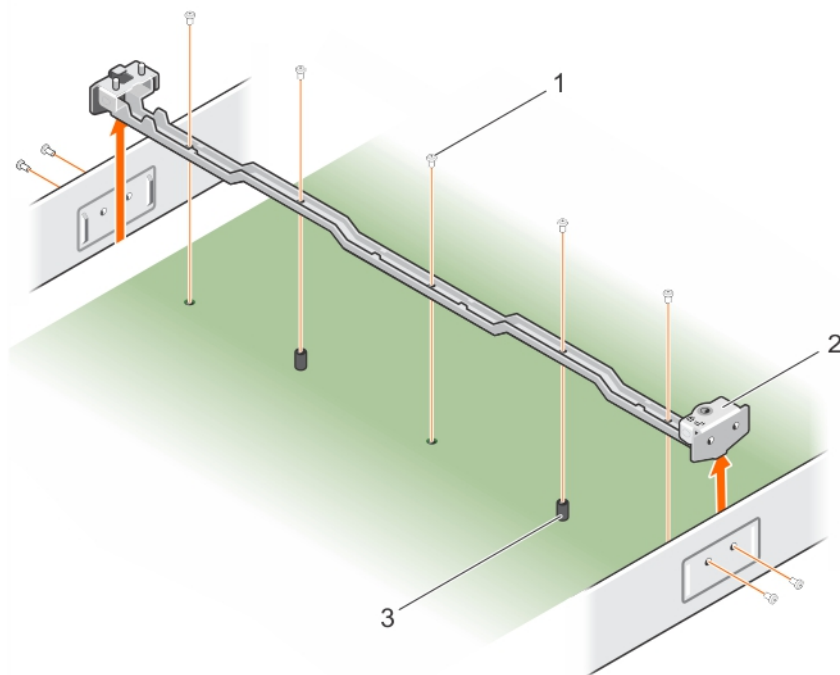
Entfernen der Haltevorrichtung des Kühlgehäuses
